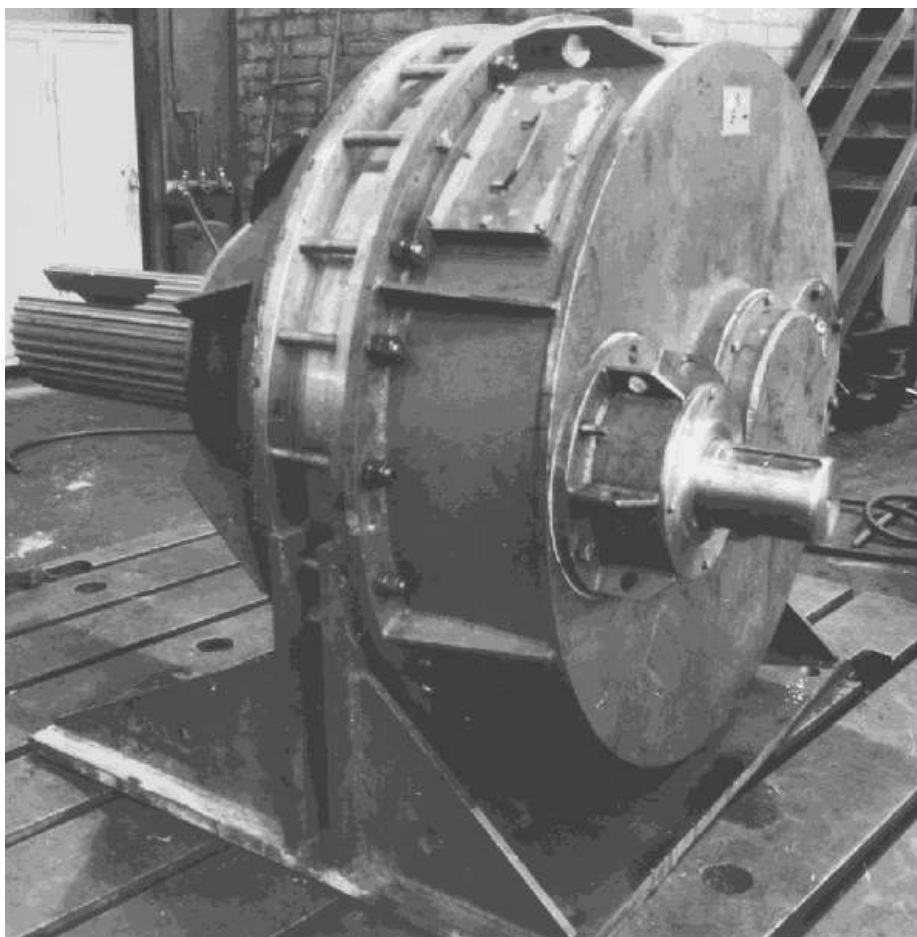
Редуктор с промежуточными телами качения привода классификатора: $N = 30$ кВт; $u = 275$
